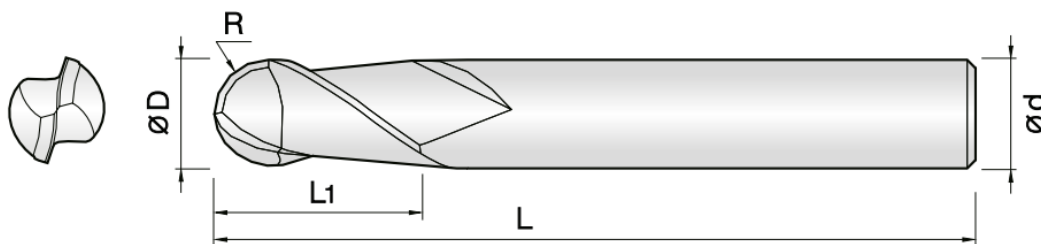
Krátka, guľová fréza do 68 HRC od PM-TECH [33].
